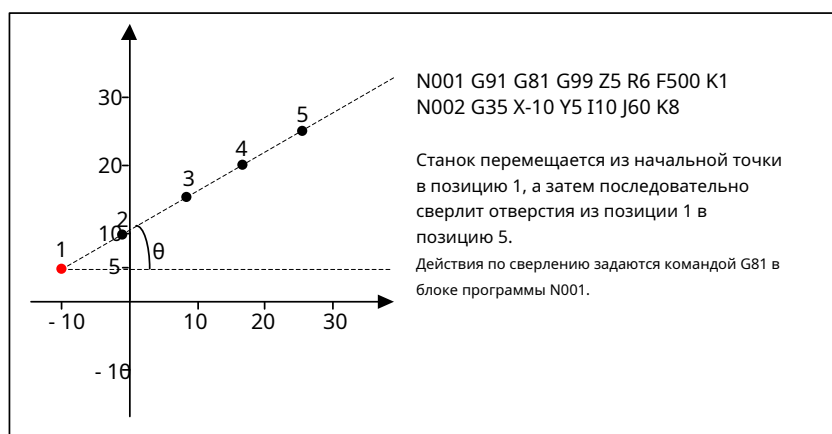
Эскиз цикла углового прямолинейного сверления
